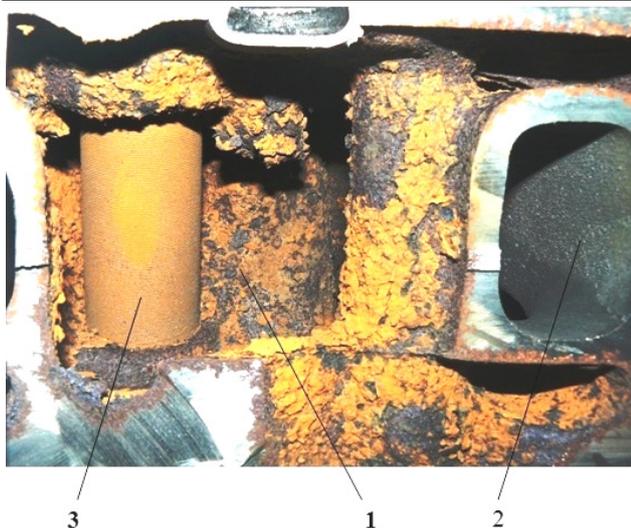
Сечение участка головки блока двигателя IVECO ($V = 3,6$ л):
